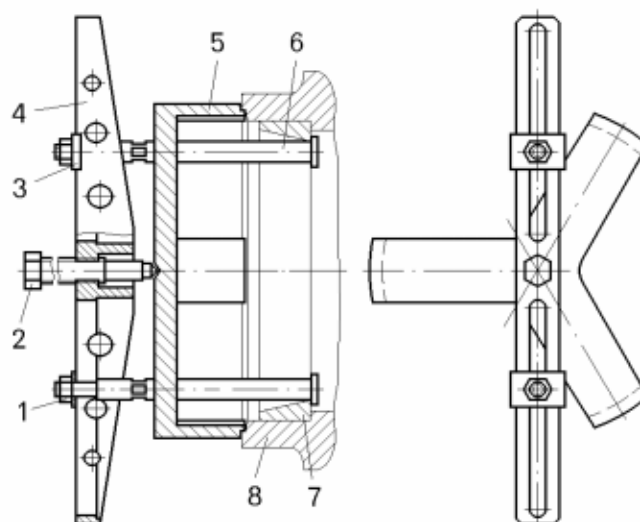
Приспособление для выпрессовки наружных колец подшипников ступиц передних колес:
